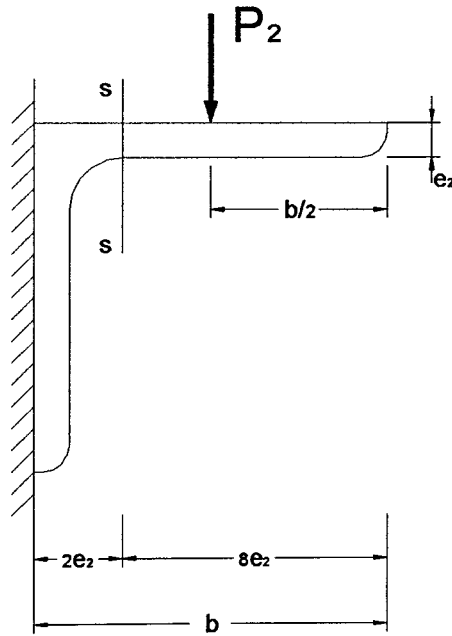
SECÇÃO TRANSVERSAL DA CANTONEIRA TIPO 2
